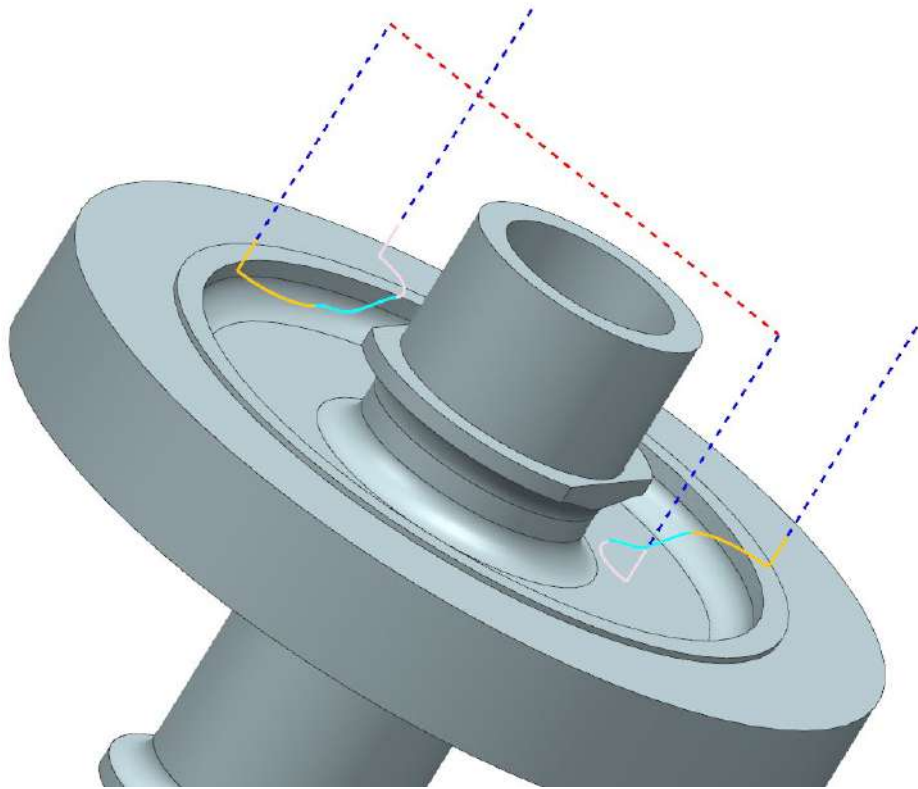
Траєкторія обробки на операцію 090 Фрезерна з ЧПК
